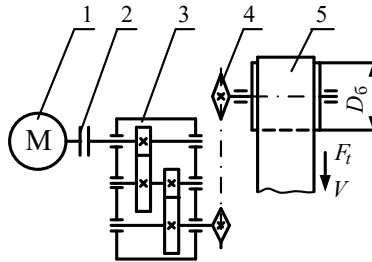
Кинематическая схема привода ленточного конвейера:
